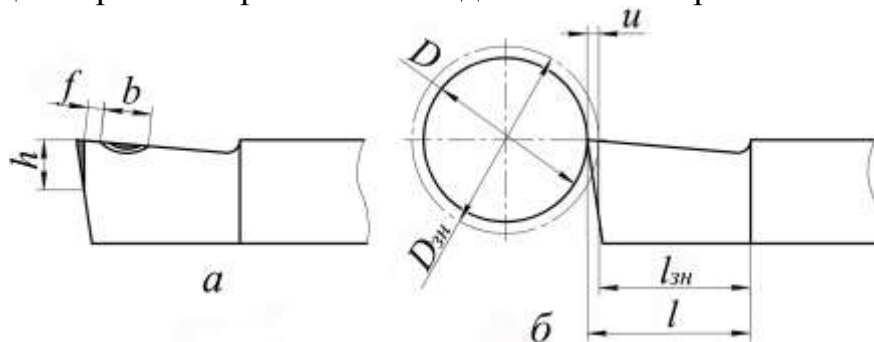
Знос різця (*a*) і зміна розмірів інструмента та заготовки при цьому (*б*)
